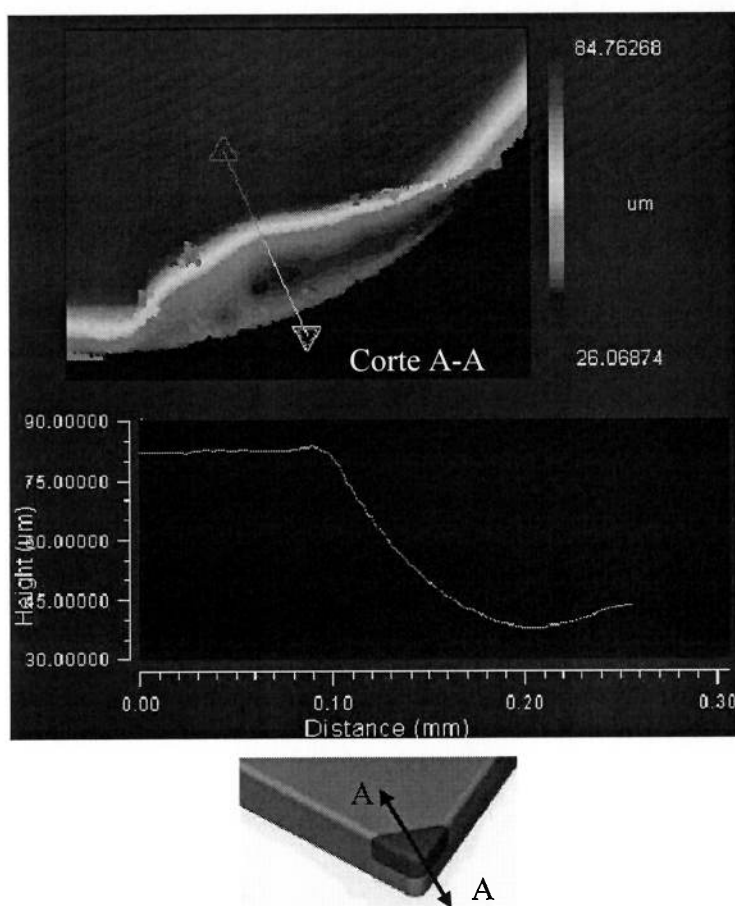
perfil da aresta de corte (condição-6); traçado com o perfilômetro Hommelwerke T8000
